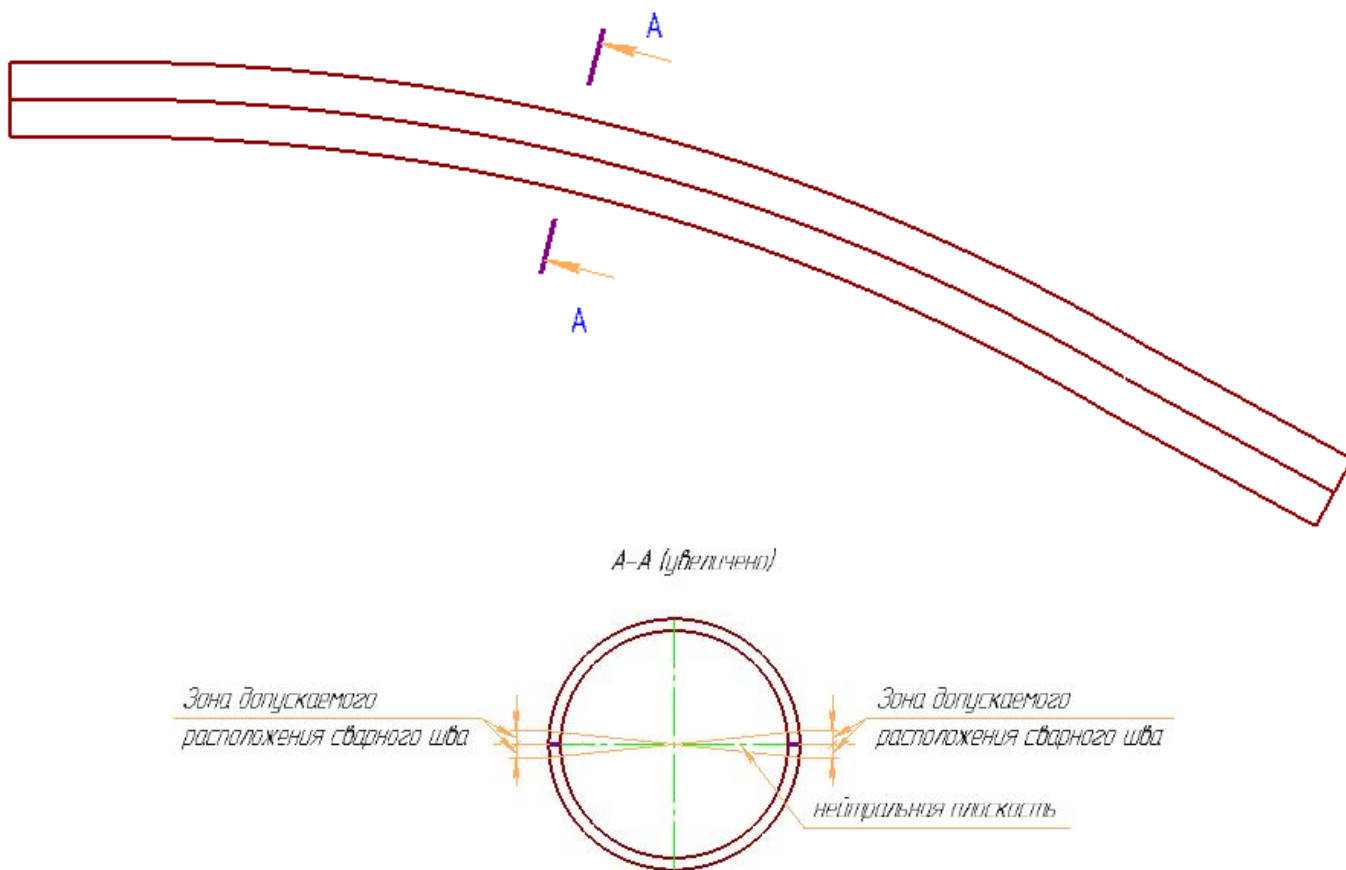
Эскиз расположения продольного сварного шва
